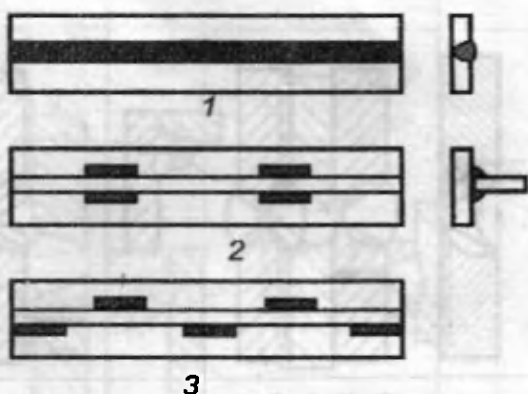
Классификация сварных швов по протяжённости: 1 – непрерывный; 2 – цепной; 3 – шахматный
